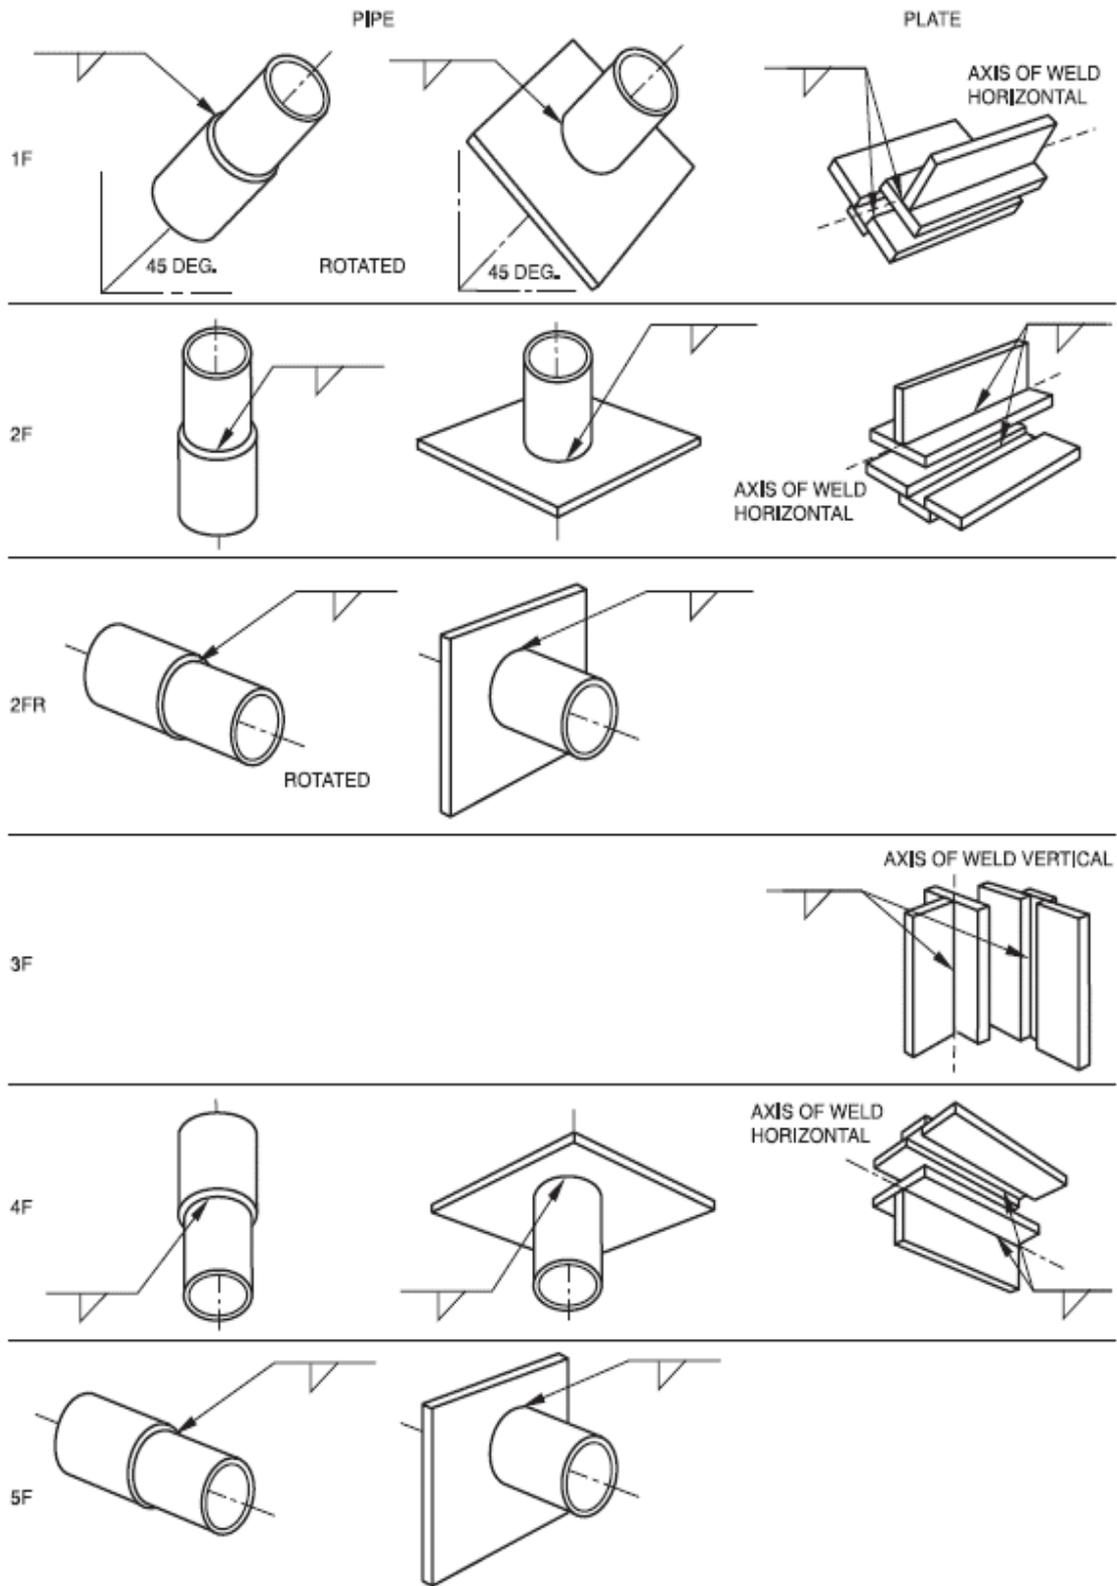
Posiciones para pruebas de soldadura en filete.
